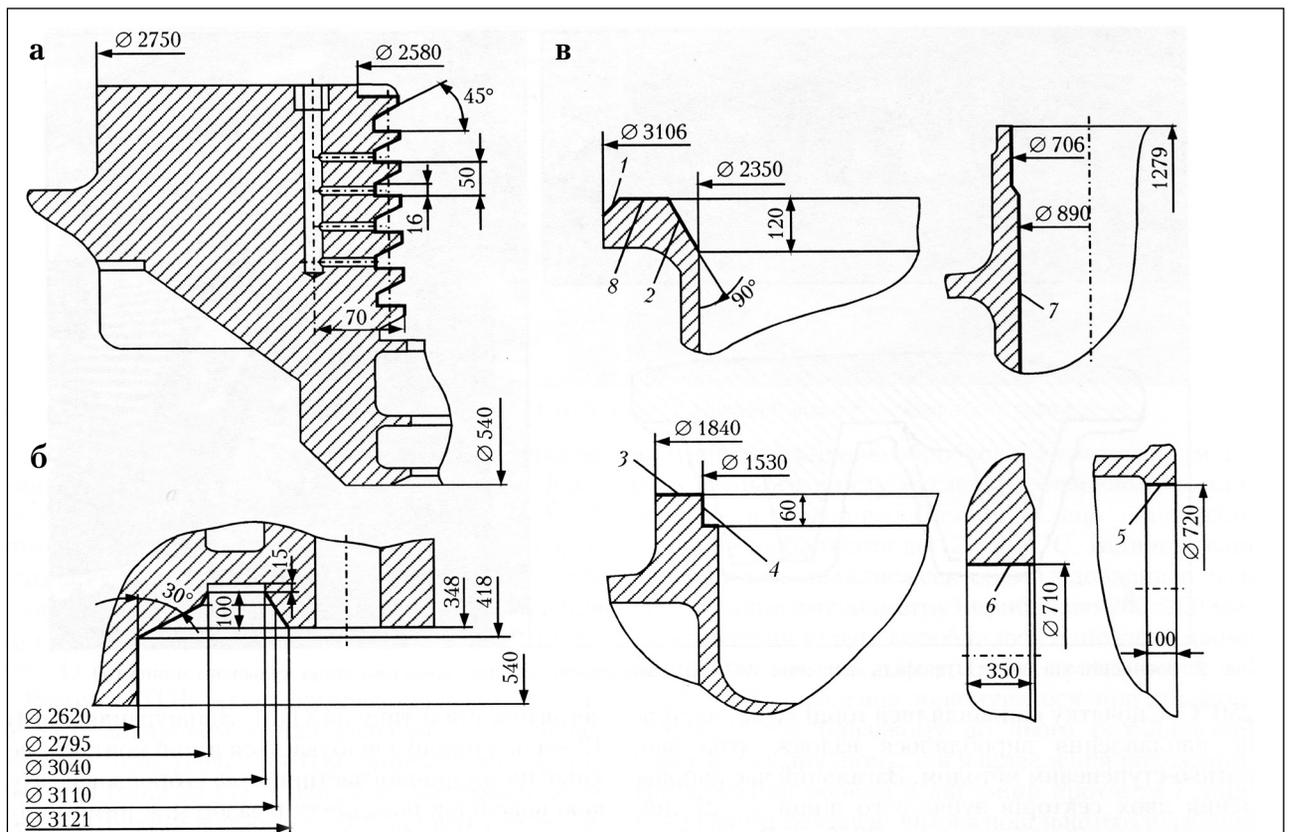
Схематическое изображение корпуса кольца (а, б) и станины (в) (наплавляемые поверхности обозначены утолщенными линиями)
